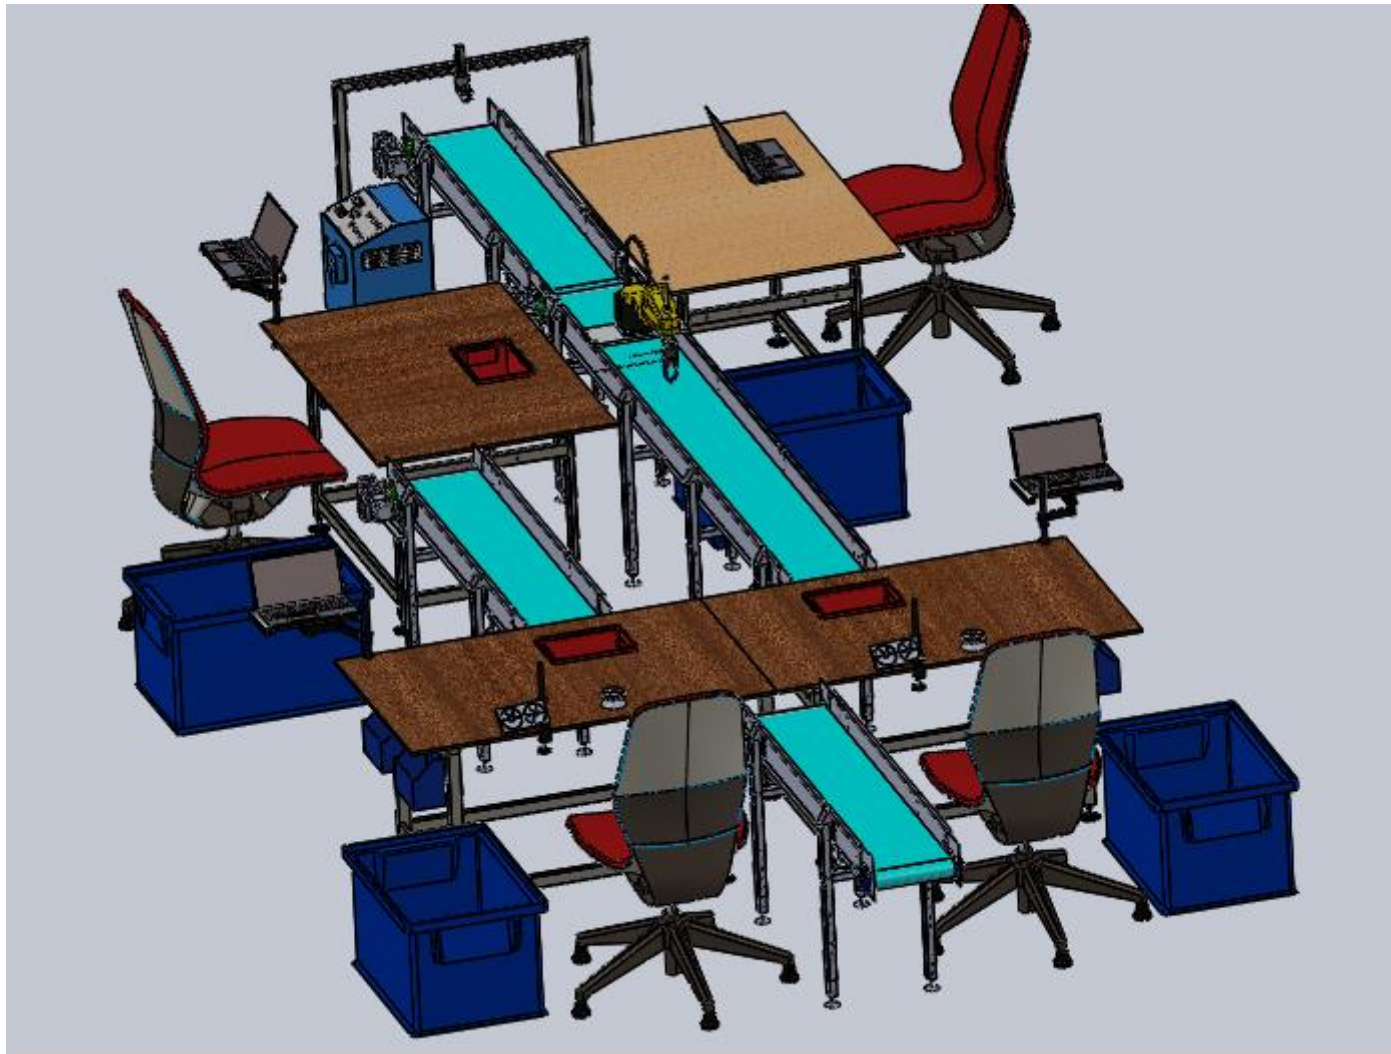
Vista des del final del layout millorat de la línia completa. Font pròpia
